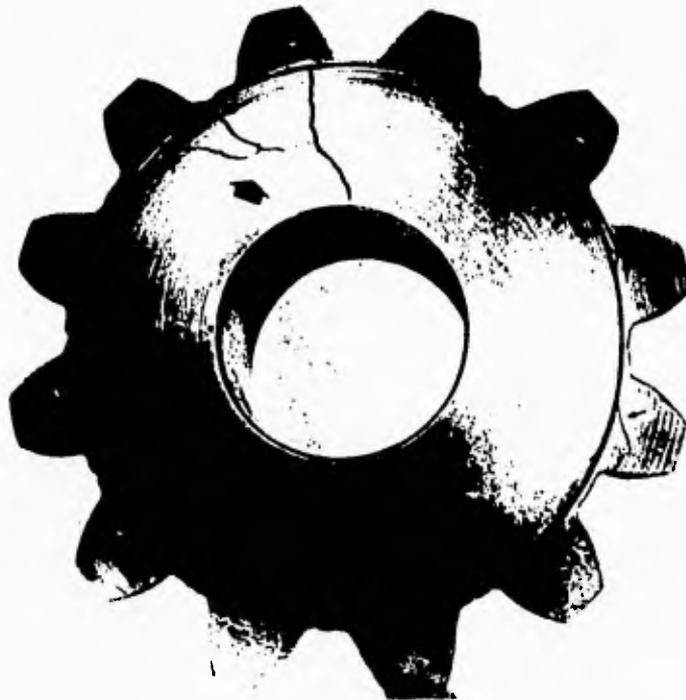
Indicaciones (vía húmeda). Grietas de temple en un piñón.
